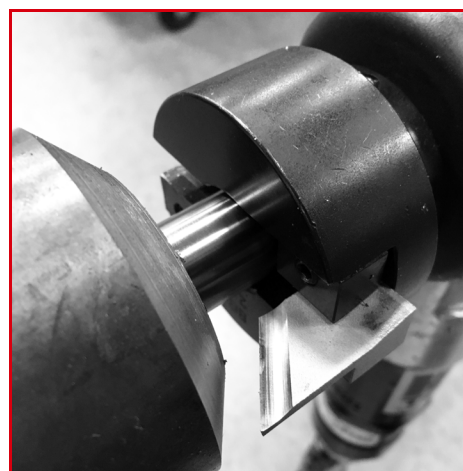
LAME DE COUPE INSTALLÉE
